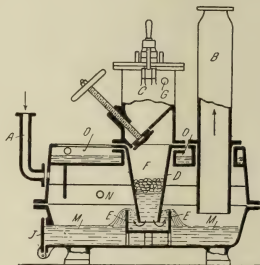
Schwefelofen der SACHSEN-BURGER MASCHINENFABRIK, Sachsenburg-Heildungen.
